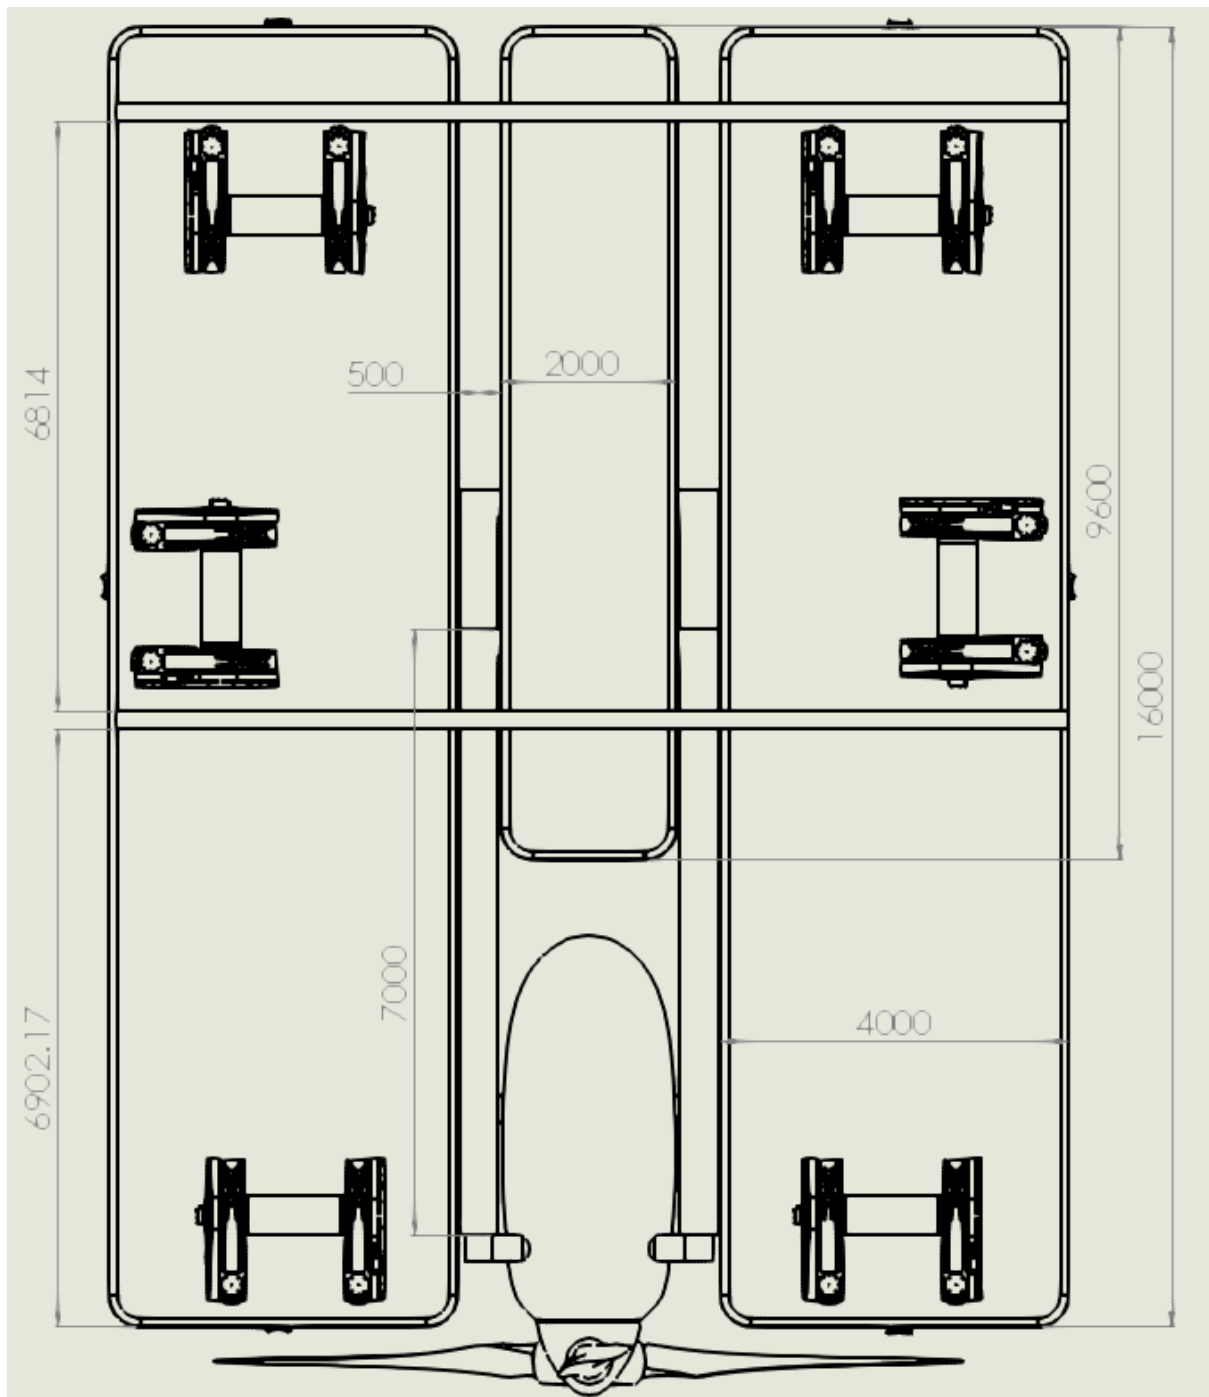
Vista superior do sistema em manutenção com dimensões em [mm].
